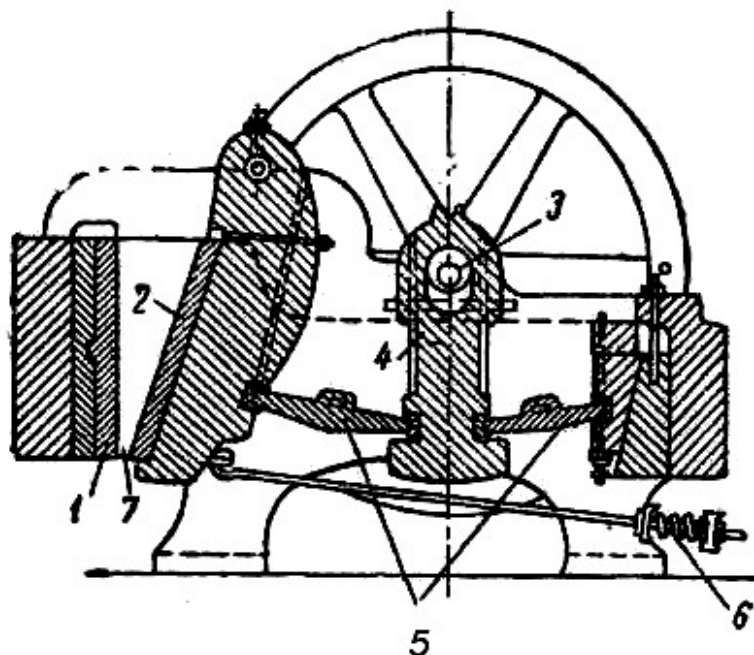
Щековая дробилка: 1 – неподвижная щека; 2 – подвижная щека; 3 – вал с эксцентриком; 4 – шатун; 5 – распорные доски; 6 – пружина; 7 – разгрузочная щель
